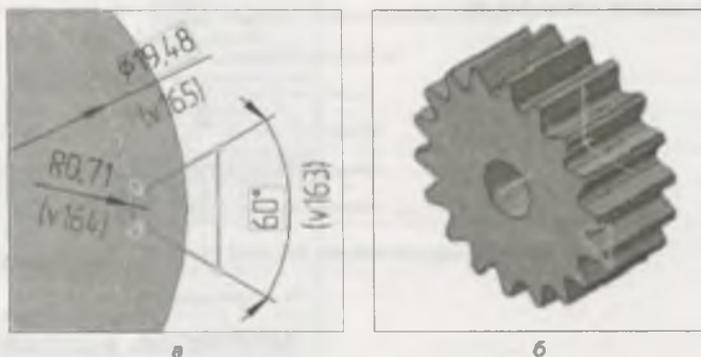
Эскиз зуба шкива (а); зубчатое колесо (б)
